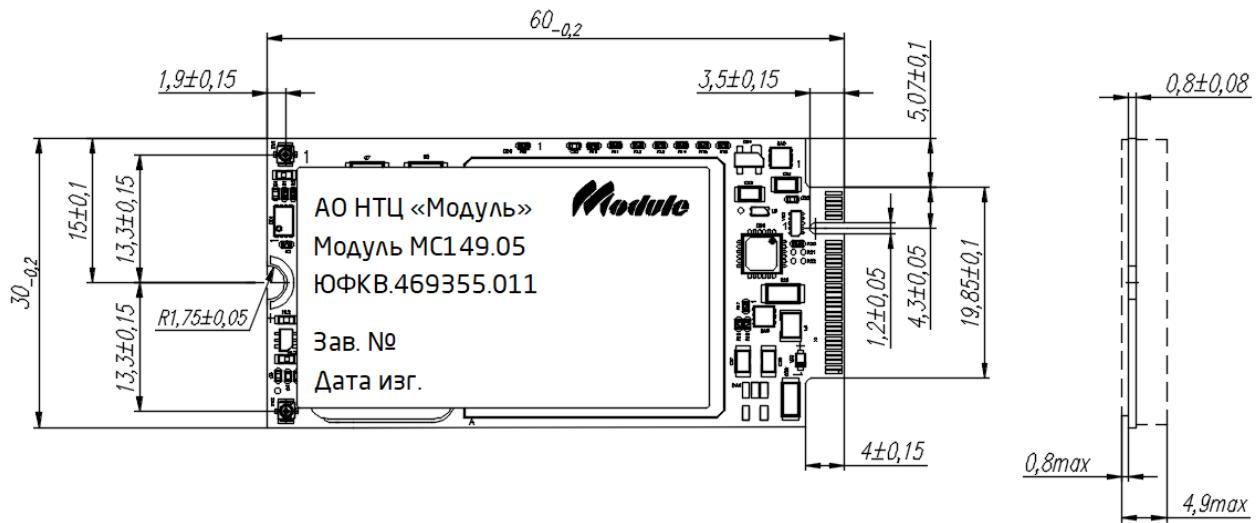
Габаритные и присоединительные размеры Модуля
